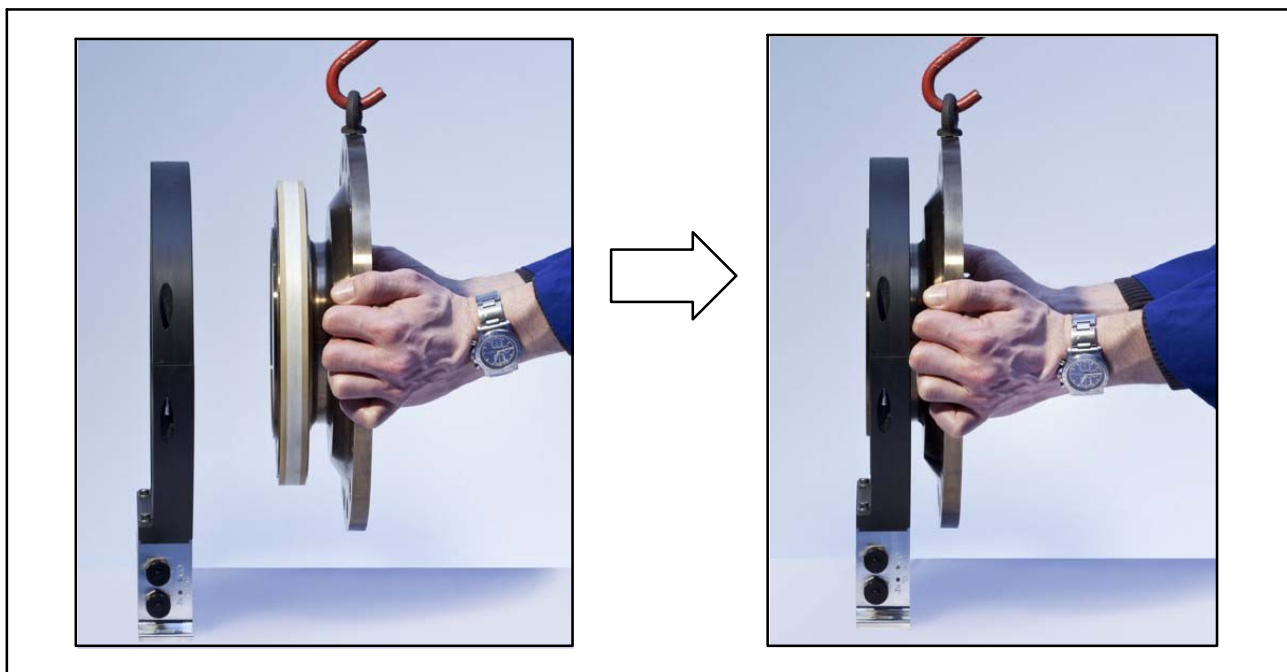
Ausrichten des Rotors mit dem Stator
